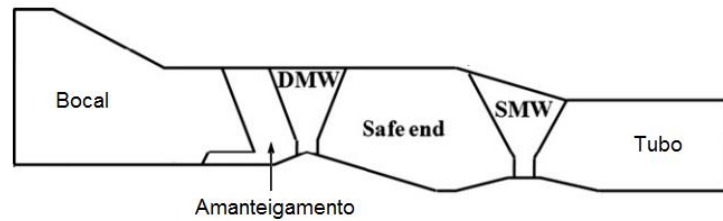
Solda dissimilar com uso de *safe end* (KIM et al 2011).
